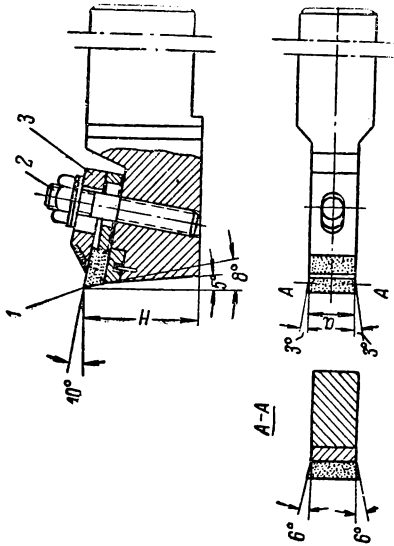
Прорезной резец с механическим креплением твердосплавной пластинки (конструкция ЦНИИТМАШ).
